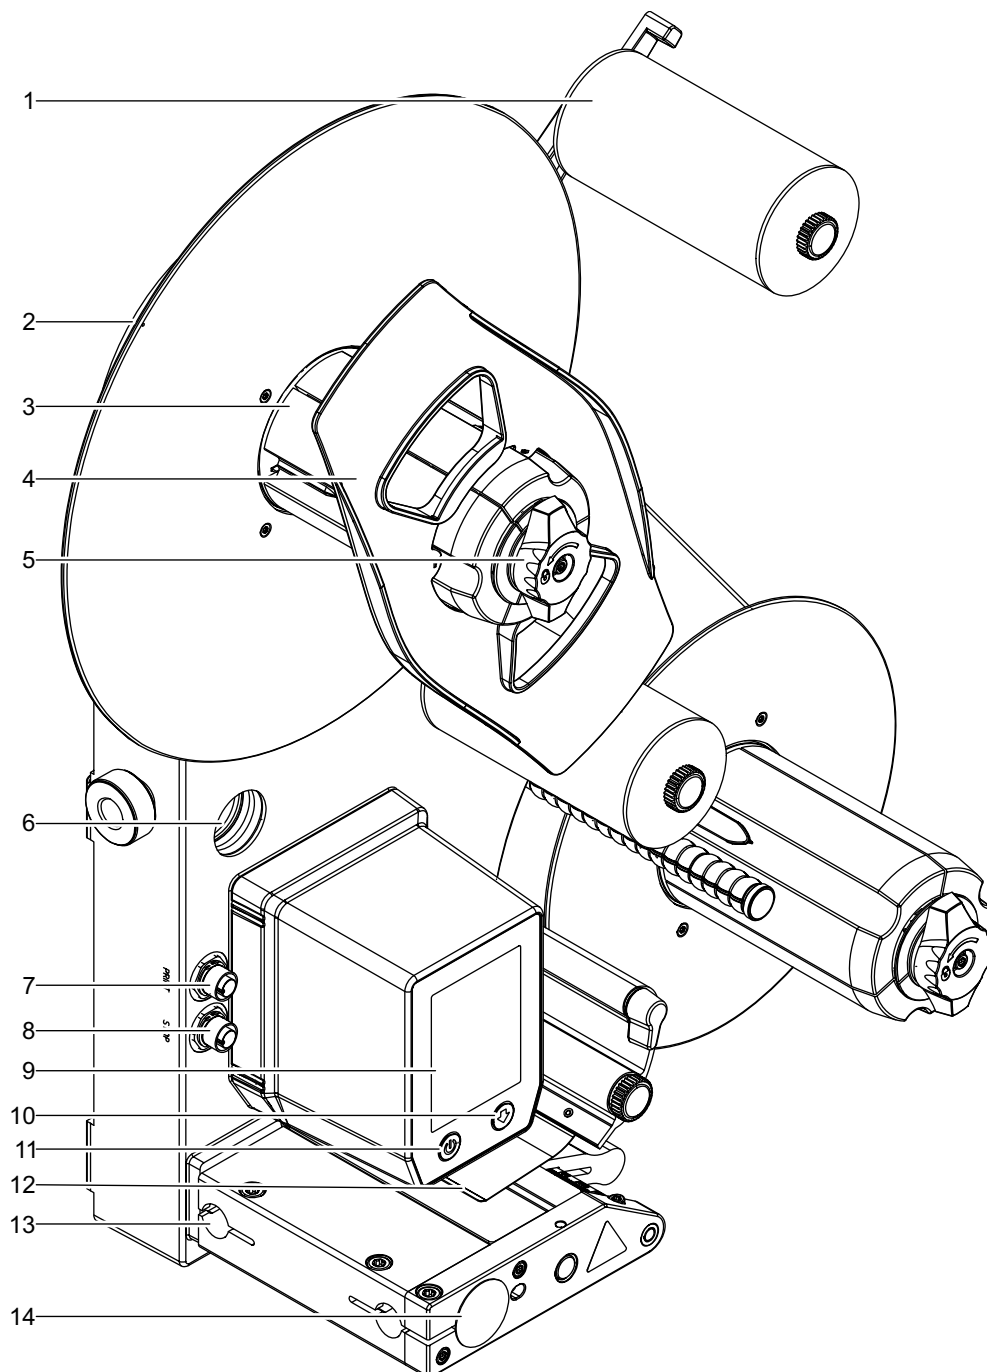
Vue d'ensemble étiqueteuse, vue côté gauche
